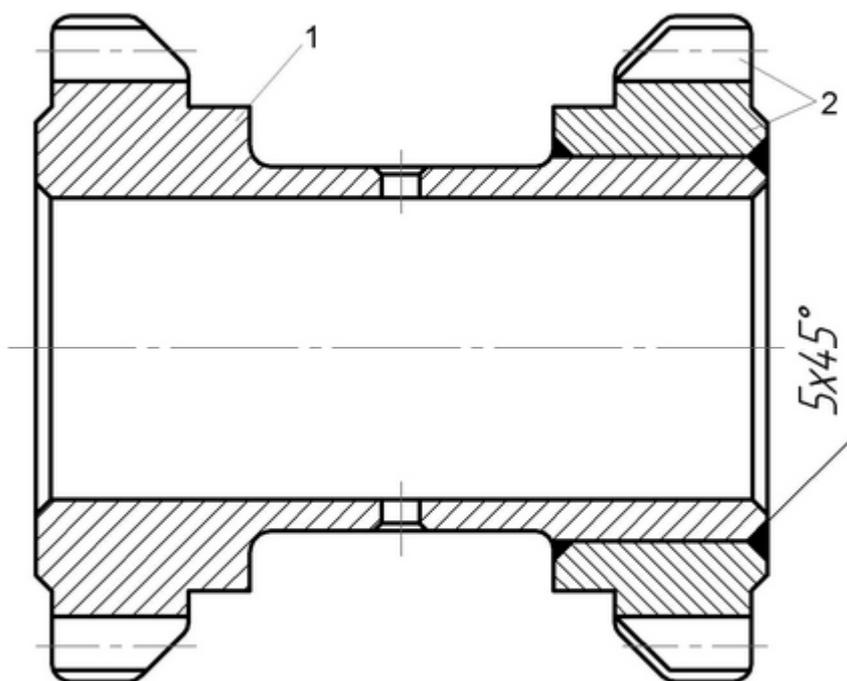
Восстановление блока шестерен коробки передач постановкой зубчатого венца: 1 – шестерня; 2 – венец
